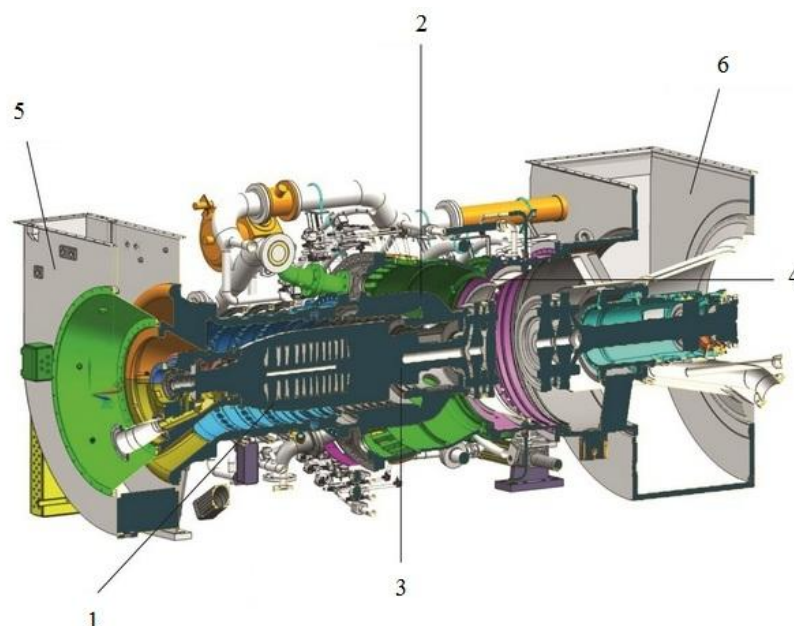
Продольный разрез газотурбинного двигателя Т16.
